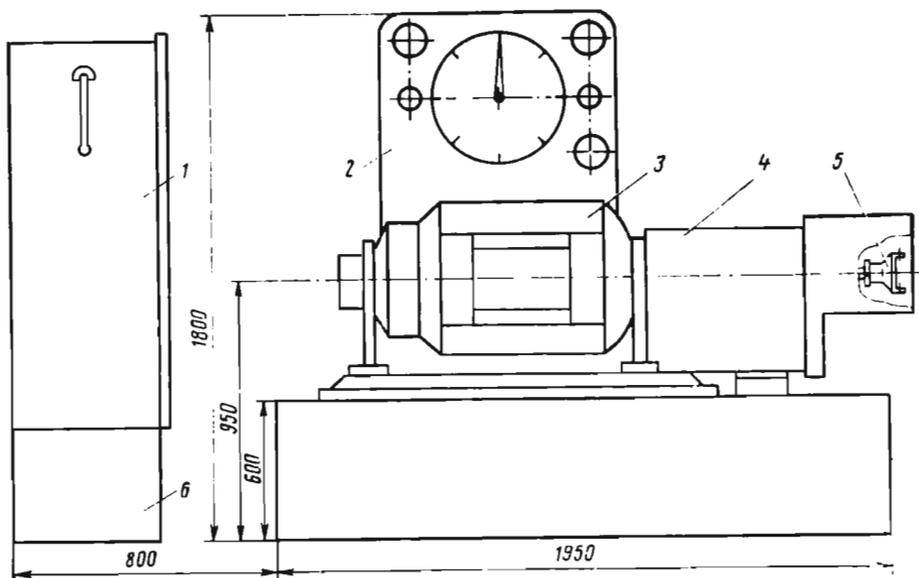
Стенд для испытаний двигателей внутреннего сгорания после ремонта: 1 — электрошкаф; 2 — измерительное устройство с приборами; 3 — балансирующая машина; 4 — кожух; 5 — карданная передача; 6 — реостат
